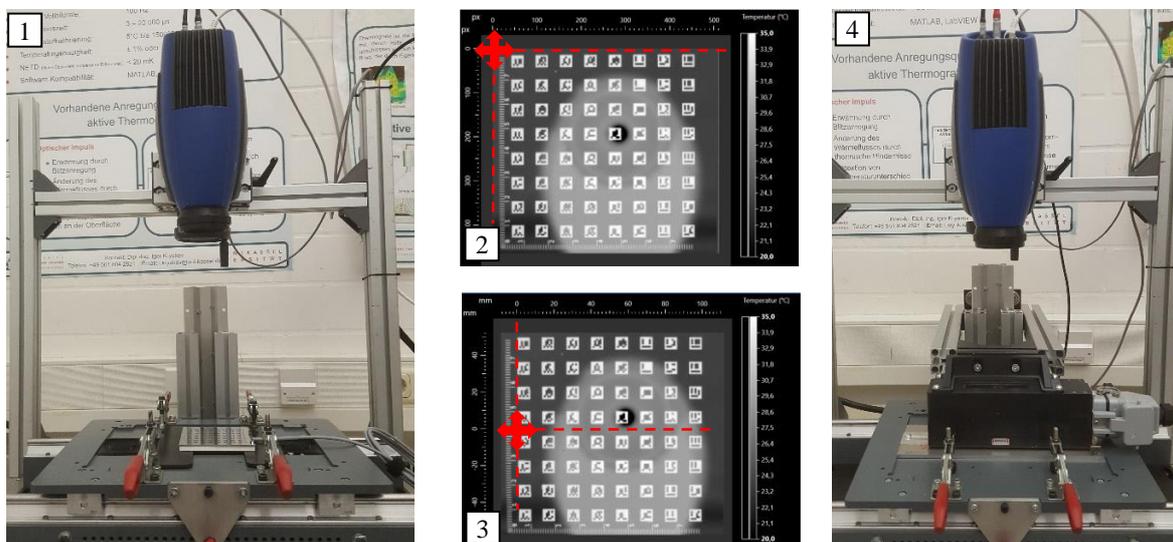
Metrische Kalibrierung des Sichtfeldes zur Prüfung von Schweißverbindungen.
